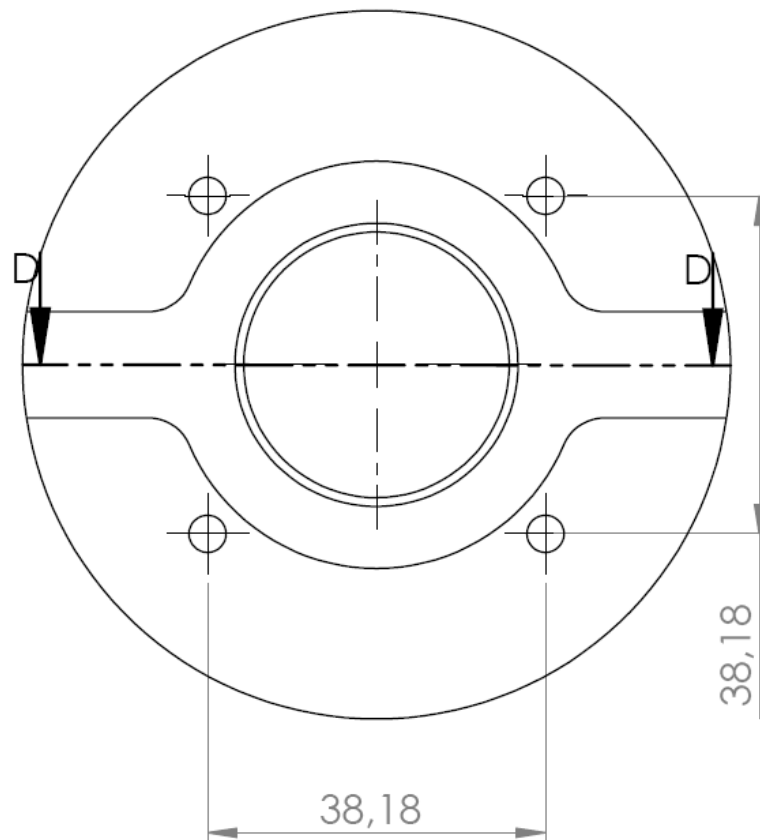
Parte superior do cabeçote – vista de cima (desenho 2)
